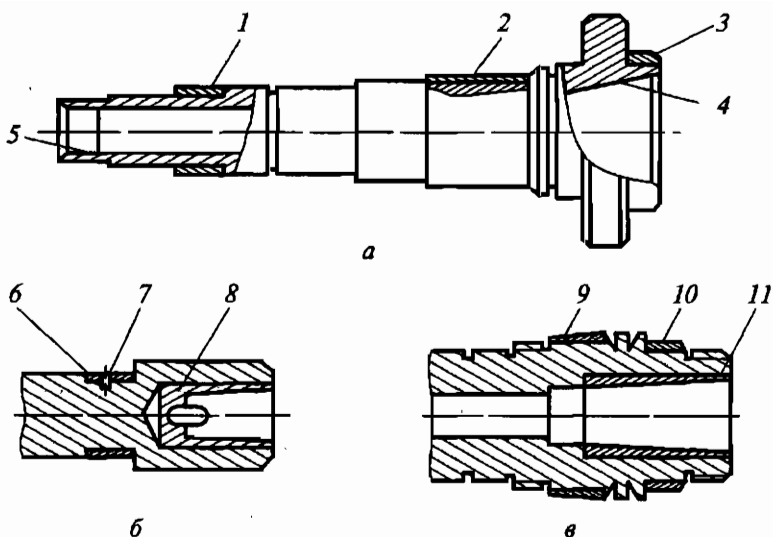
Схемы ремонта шпинделей токарных (а, в) и сверлильного (б) станков:
